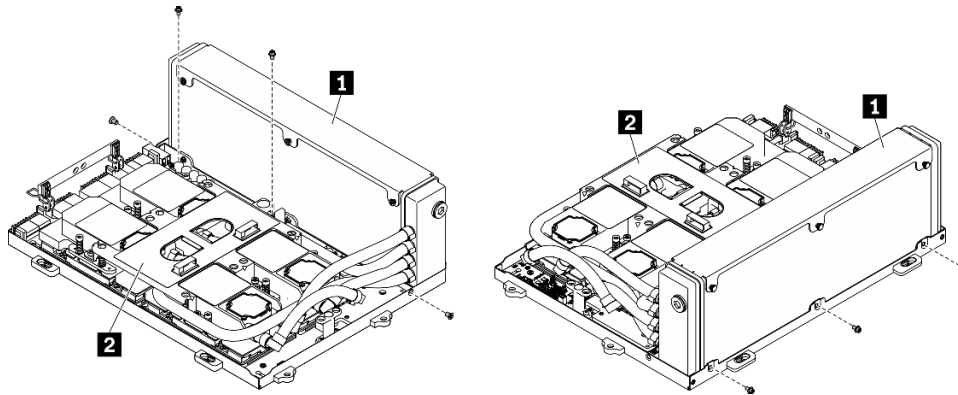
Entfernen der GPU-L2A-Baugruppe
